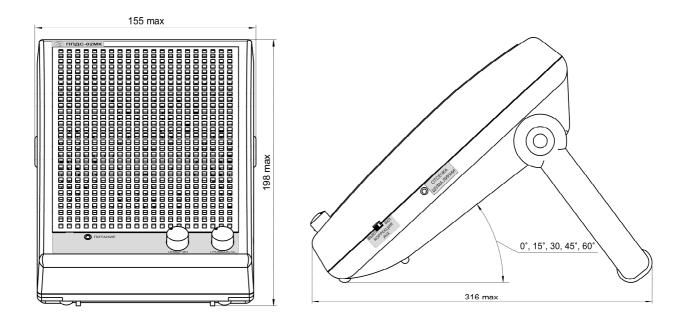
Внешний вид, установочные и габаритные размеры ППДС
